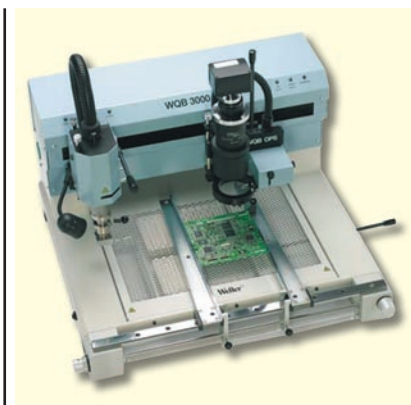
Ремонтный комплекс для микросхем типа BGA WQB3000
